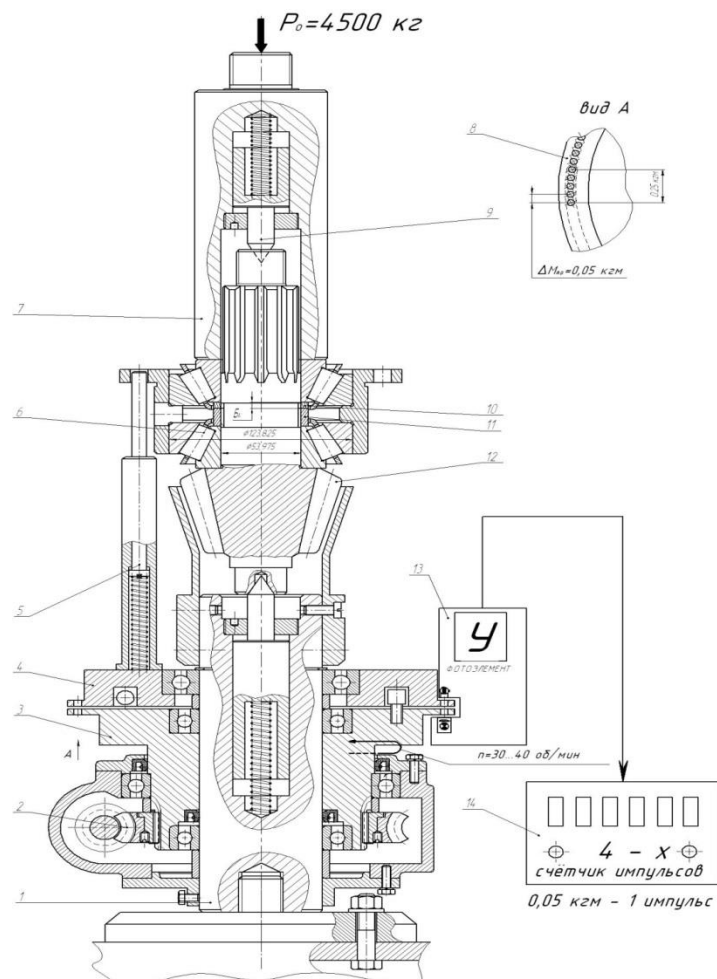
Опытно-экспериментальная установка для измерения требуемого размера компенсатора в подшипниковом узле ведущей шестерни редуктора среднего моста автомобиля «Камаз-5320»
